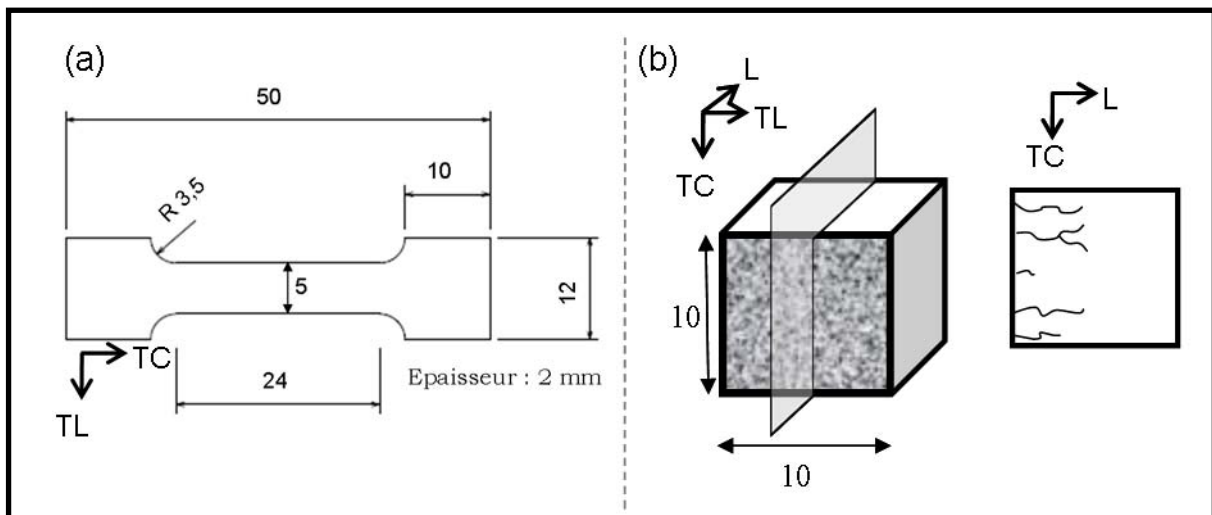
Schéma des échantillons utilisés pour caractériser l'endommagement par corrosion : (a) éprouvette plate de traction, (b) cube. Dimensions en mm.
